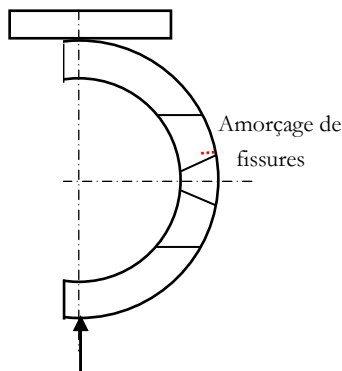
zone d'amorçage des fissures sur maquettes soudées
